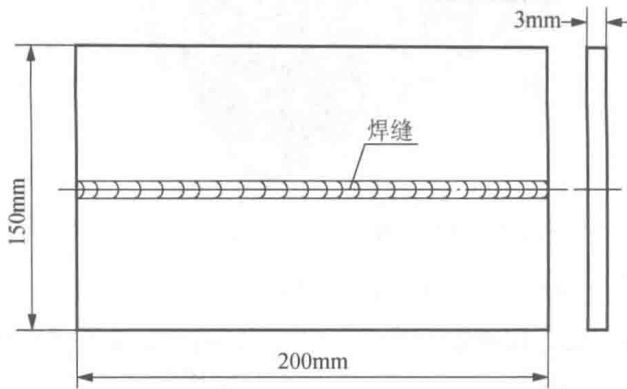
不锈钢板表面 MIG 堆焊示意图
